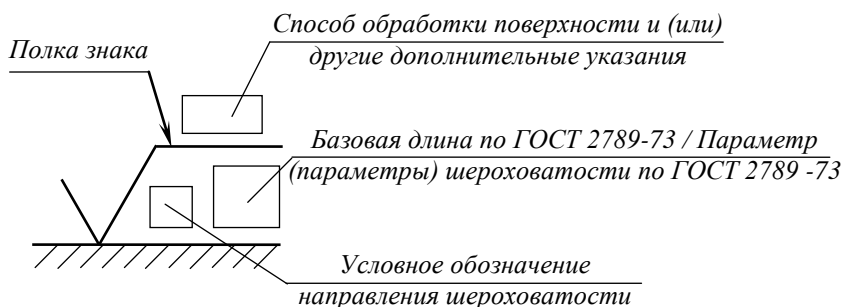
Структура обозначения шероховатости поверхности
